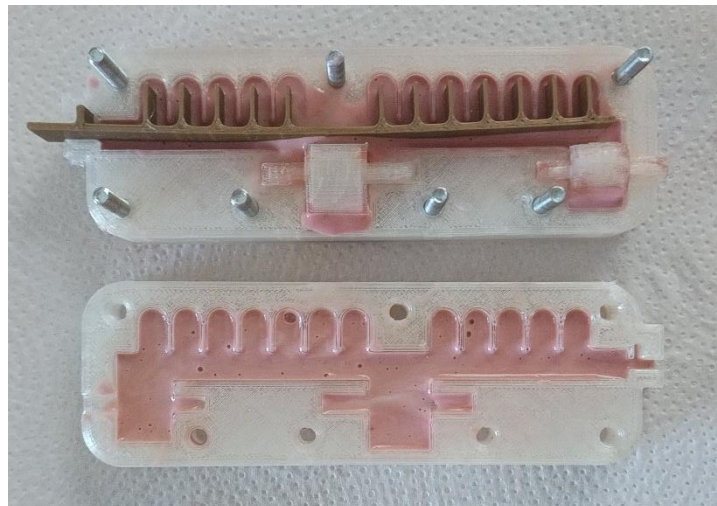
Molde negativo do atuador utilizado na moldagem do silicone Elastosil M4601 A/B®.
